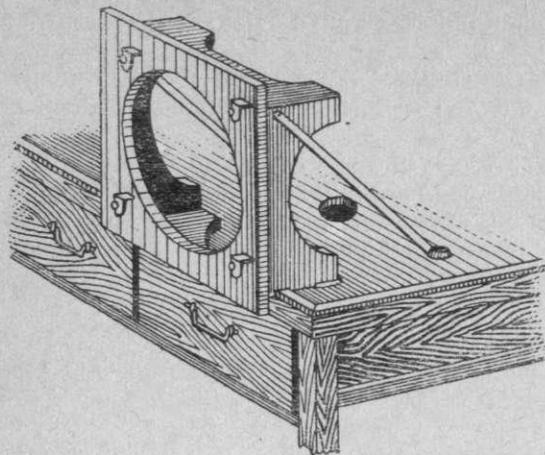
Приспособление для разборки и сборки нагнетателя мотора М-25.
